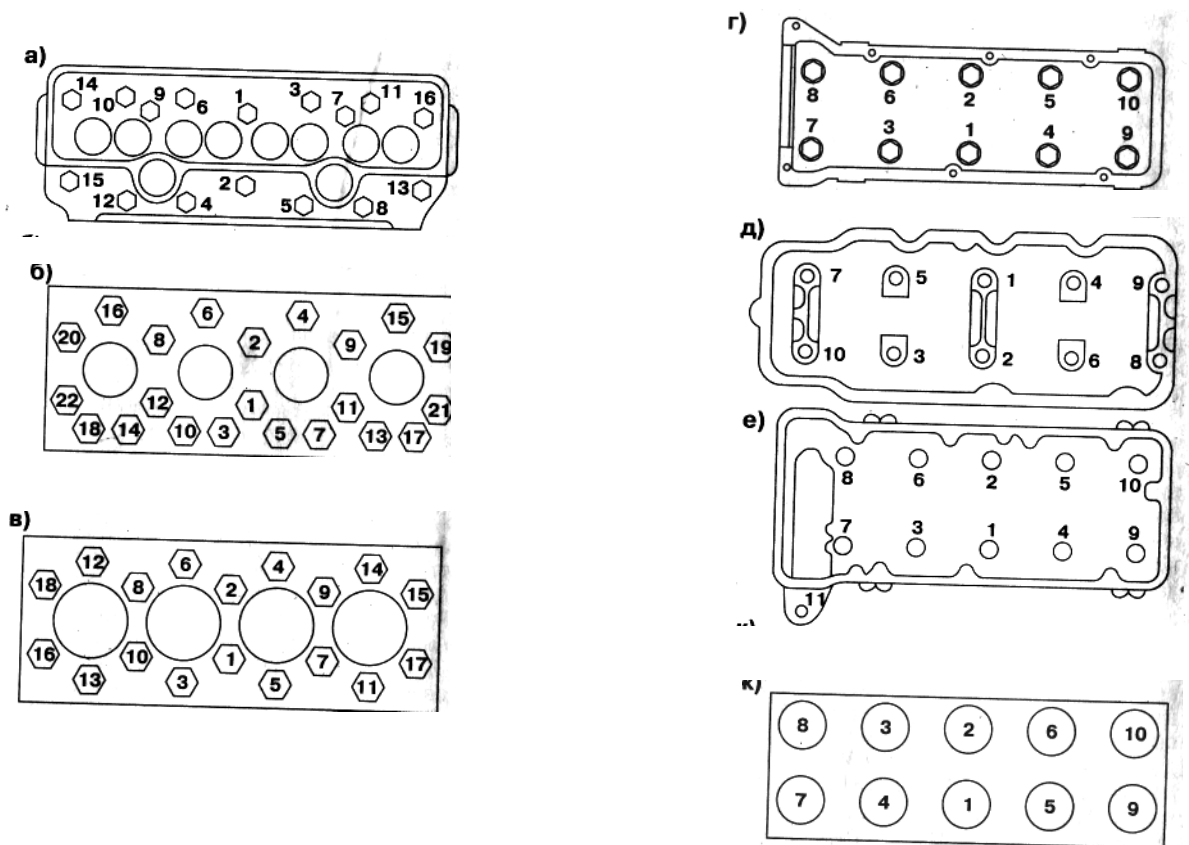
Регулировка зазоров в клапанах и проверка крепления головки цилиндров двигателя ЗМЗ-4022.
